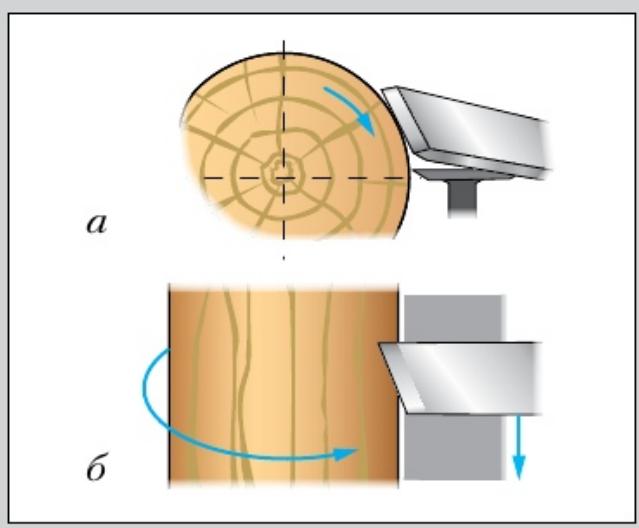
Чистовое точение косой стамеской: *а* – вид с торца заготовки; *б* – вид сверху
